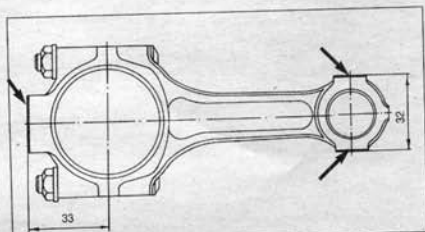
Места, на которых допускается удалять металл, при подгонке массы верхней и нижней головок шатуна
